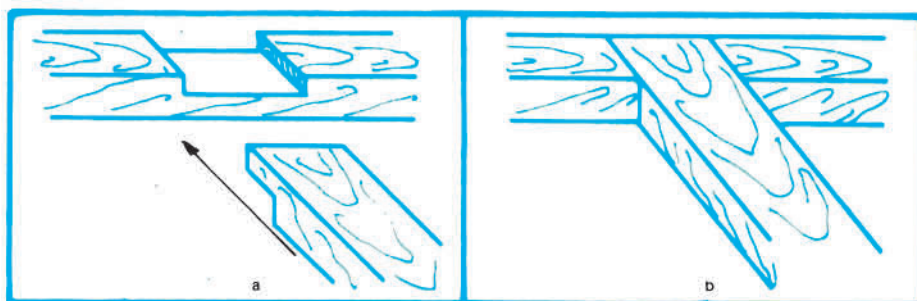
Ensamble a media madera en T: a) piezas donde se eliminó el material sobrante; b) ensablaje de las piezas.
